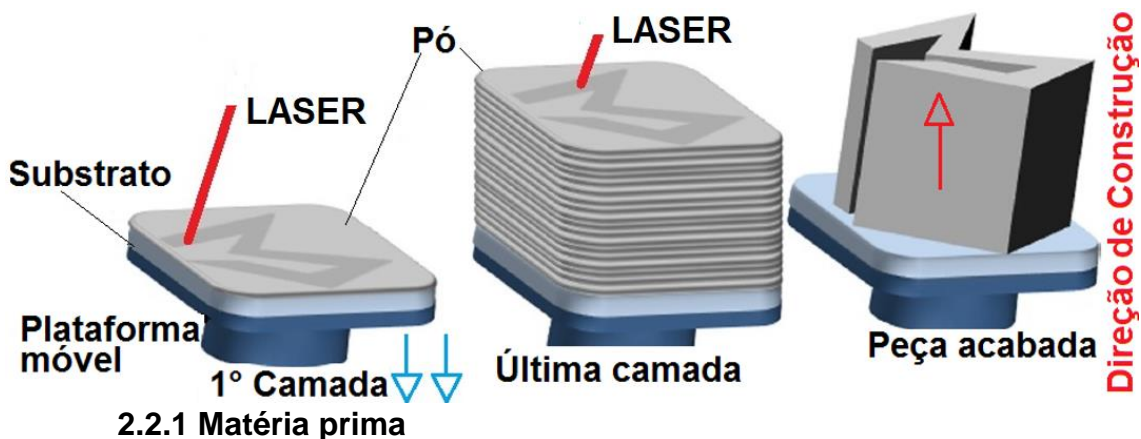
Construção da peça dentro da câmara até a retirada do pó remanescente.
